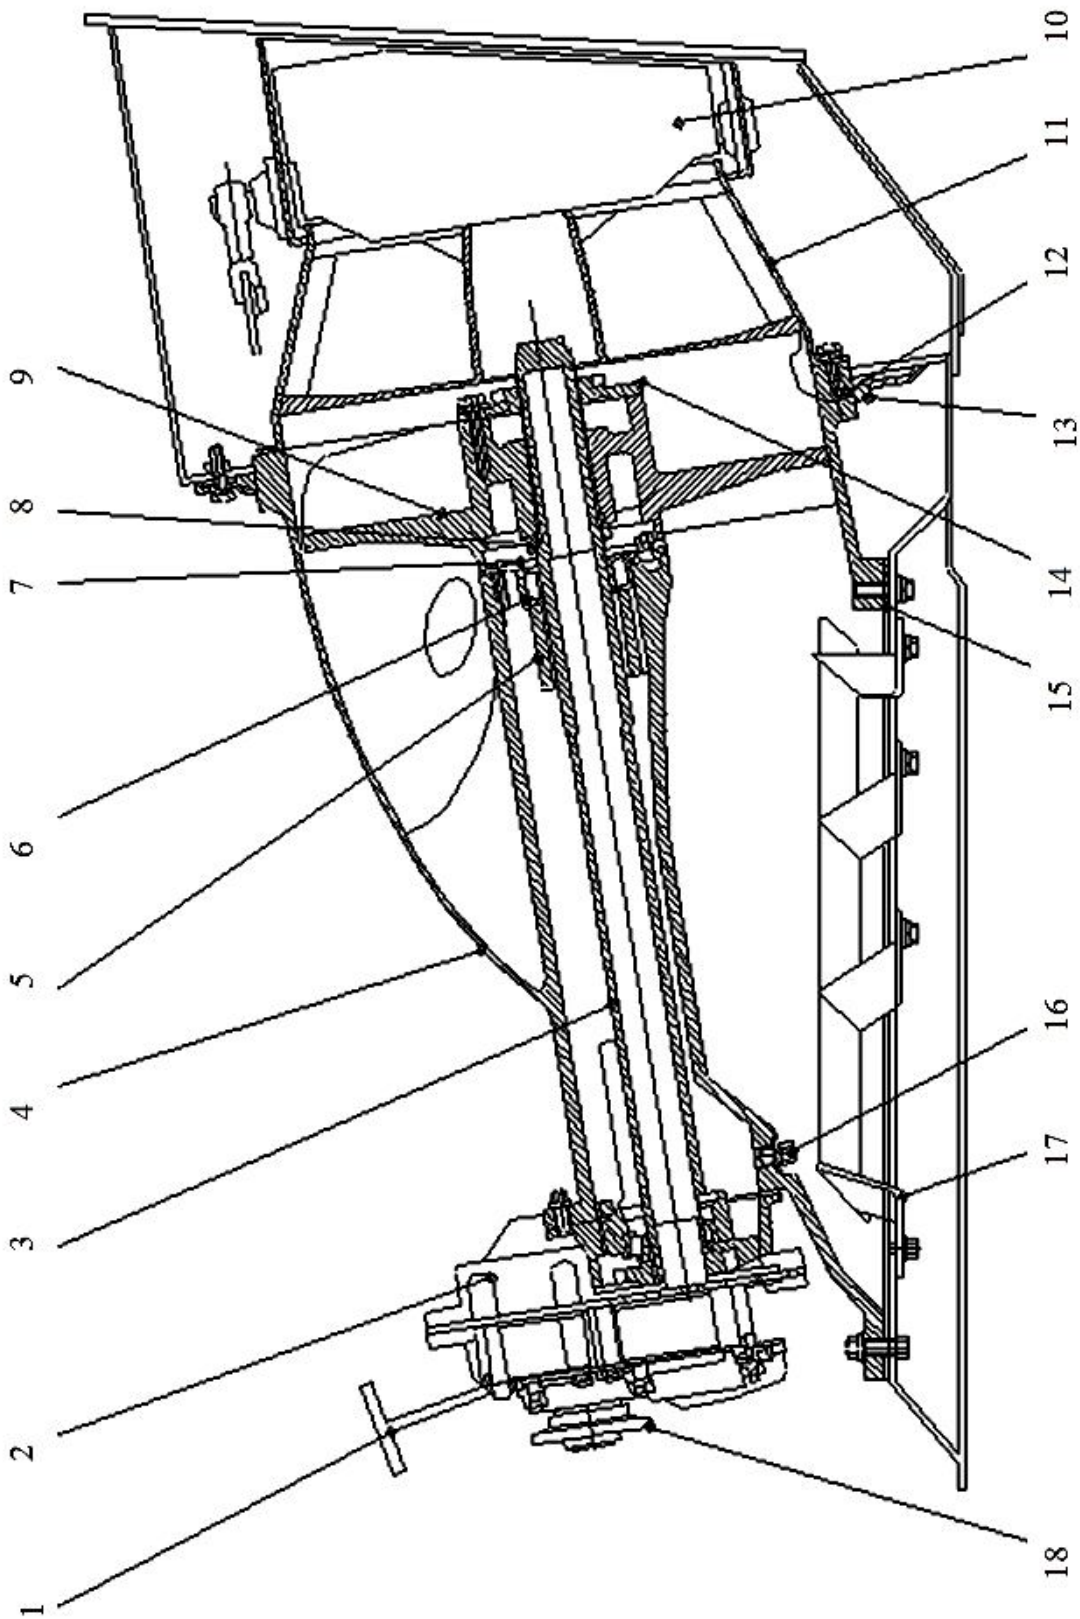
Водометний рушій. 1 – рукоятка пробки масляного отвору; 2 – редуктор; 3 – вал гребного гвинта; 4 – корпус рушій; 5 – втулка; 6 – манжети; 7 – кришка манжети; 8 – розпірне кільце; 9 – гребний гвинт; 10 – кермовий апарат; 11 – напрямний апарат; 12 – фланець; 13 – упільнювальне кільце; 14 – гайка кріплення гребного гвинта; 15 – прокладка; 16 – пробка зливного отвору; 17 – знімна захисна решітка; 18 – фланець ведучого вала
